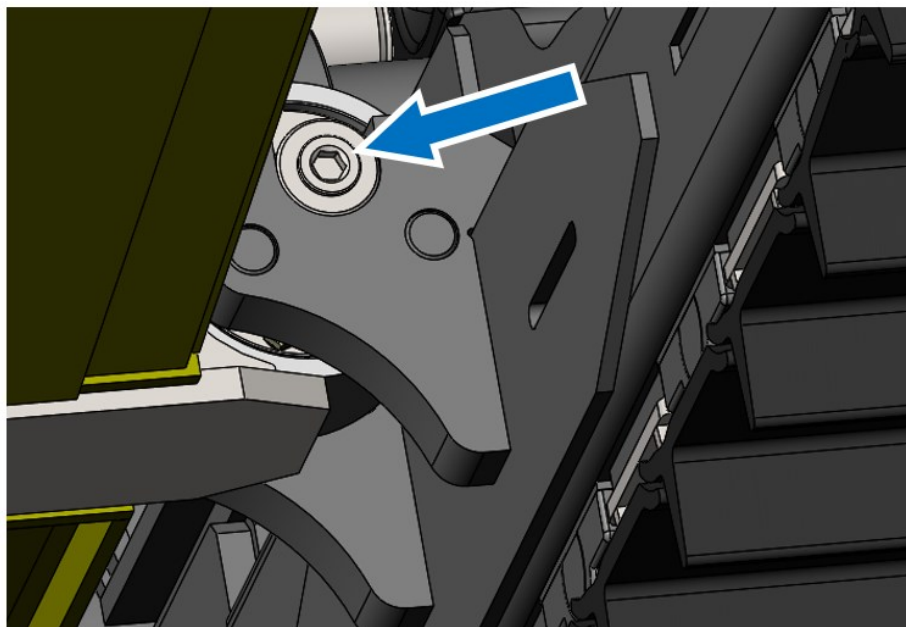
Точки смазки боковых осей балансирной балки
